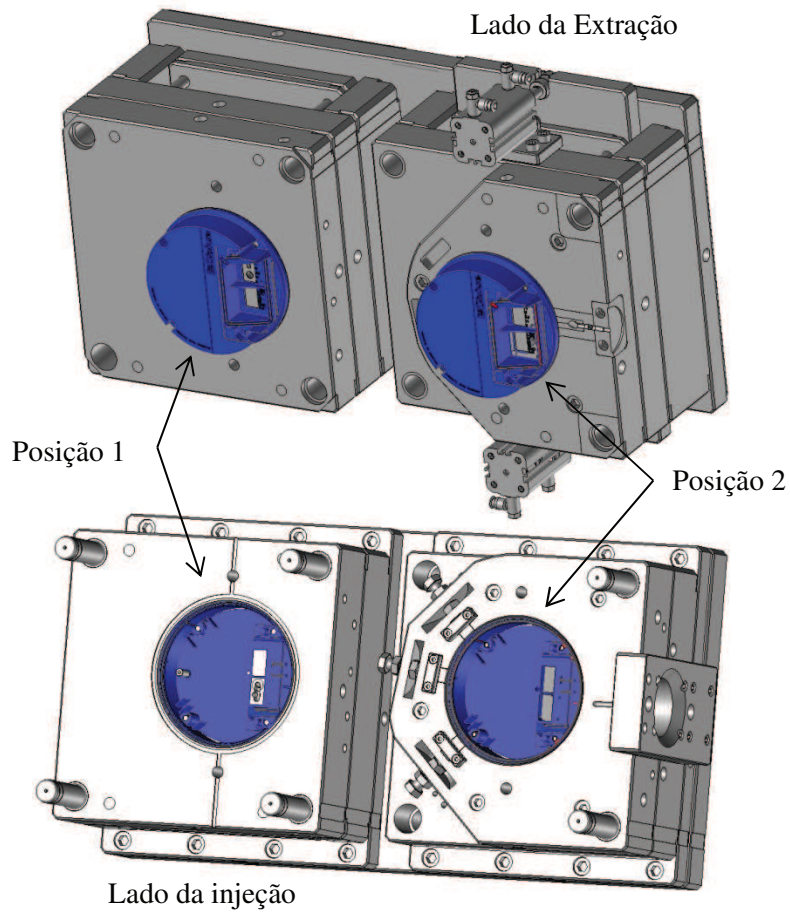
Molde bi-material, processo transferência – duas posições de injeção.
